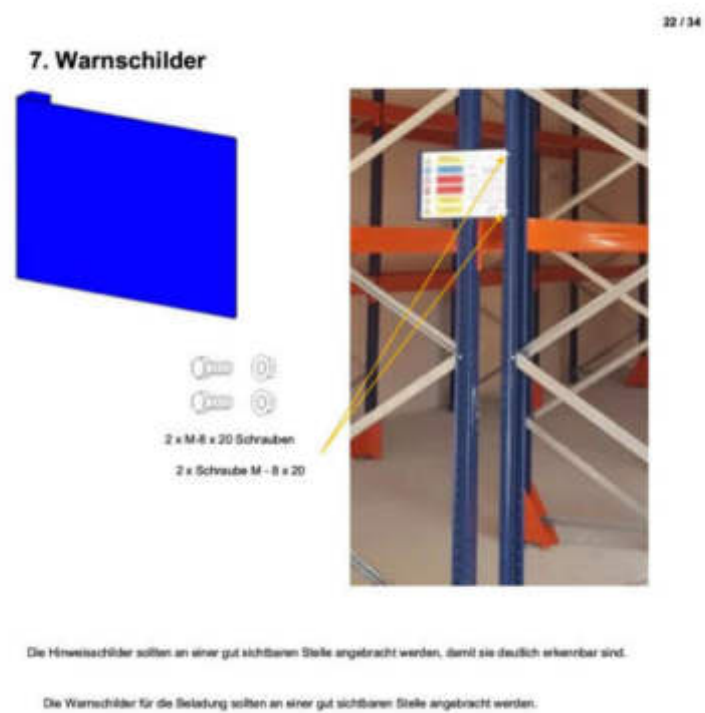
Emplacement des panneaux d'avertissement et quincaillerie de montage.
